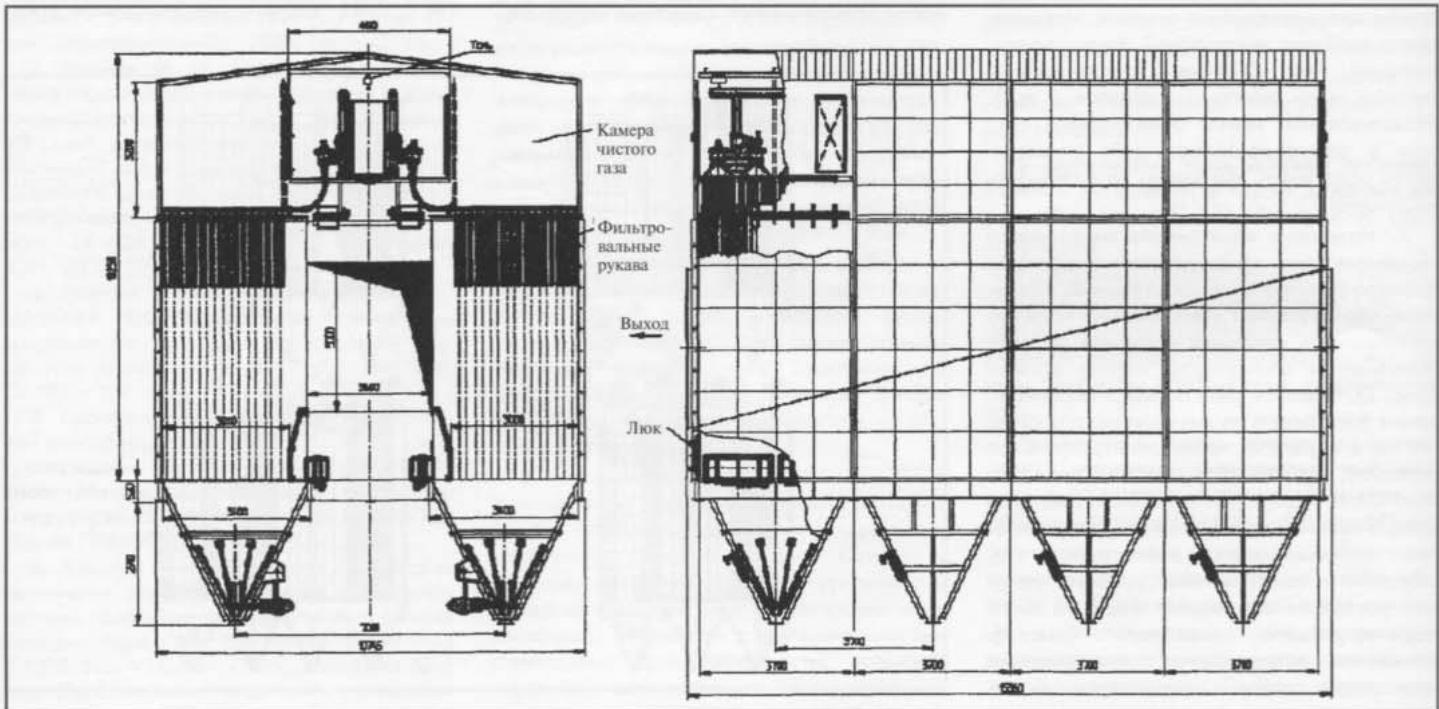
Рукавный фильтр ФРМИ-6400, 8 модулей, двухрядная компоновка
